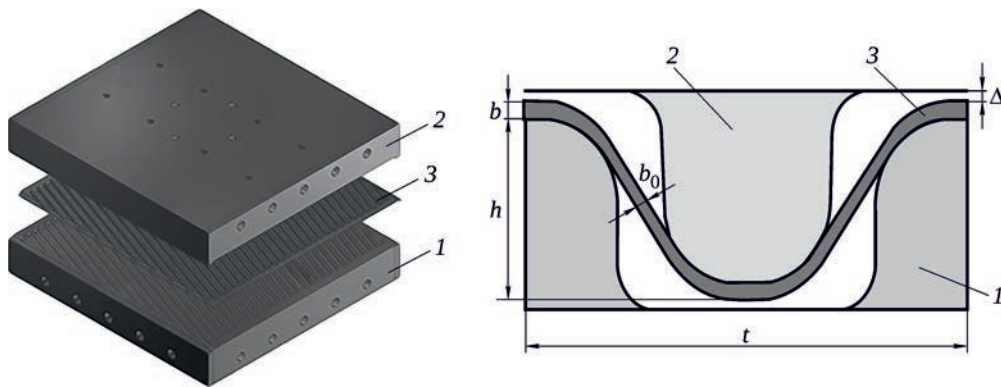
Формообразующие элементы штампа для изготовления пластин теплообменника и их геометрия:
